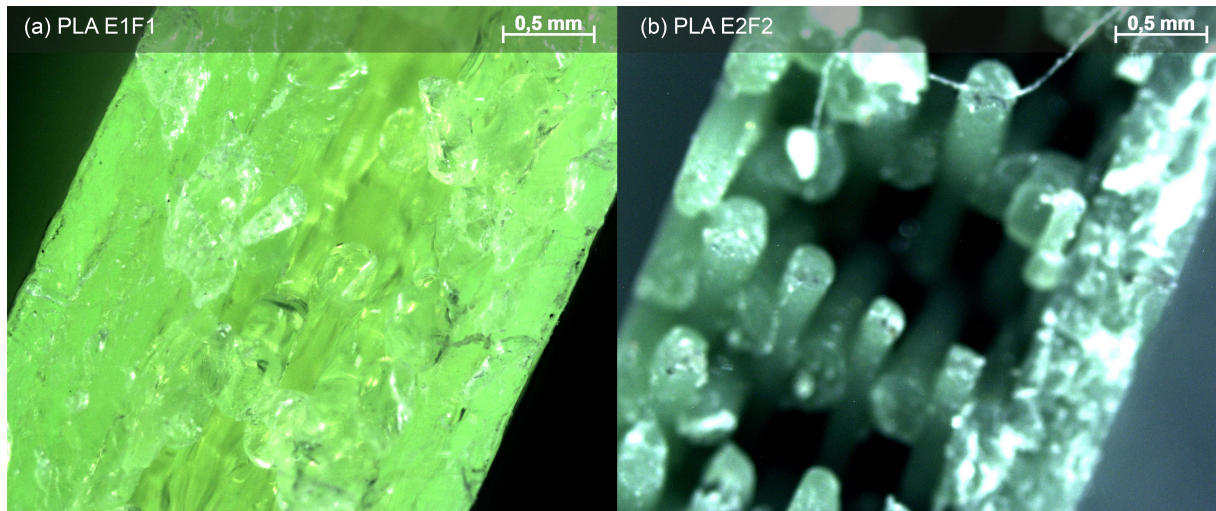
Imagem da seção transversal dos corpos de prova de PLA para ensaio de impacto.
